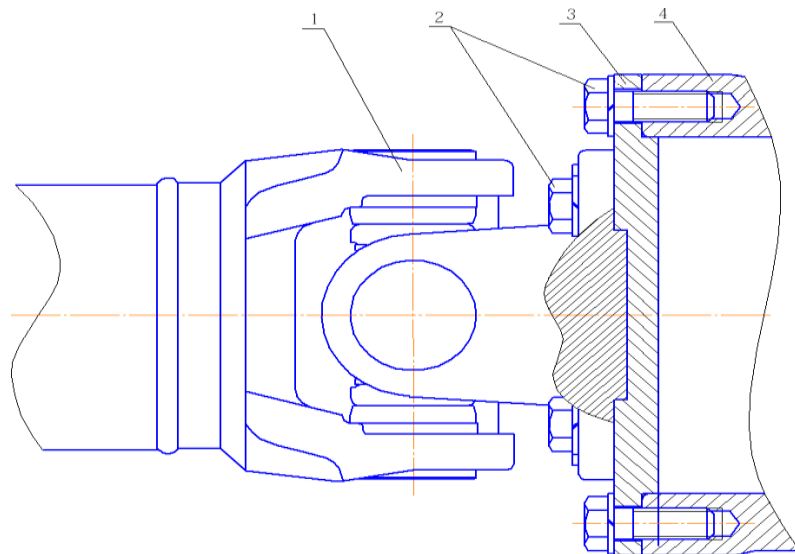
Конструктивна схема вузла з'єднання карданного вала з маховими масами:
